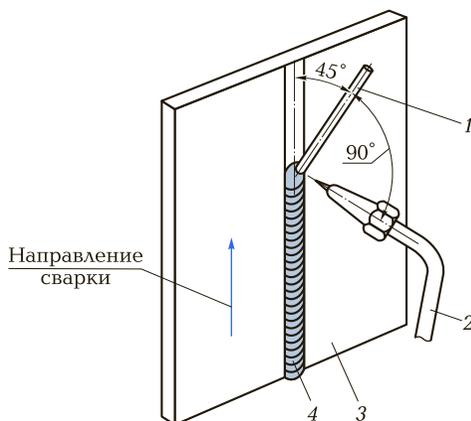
Схема сварки вертикального шва снизу вверх (левый способ):
